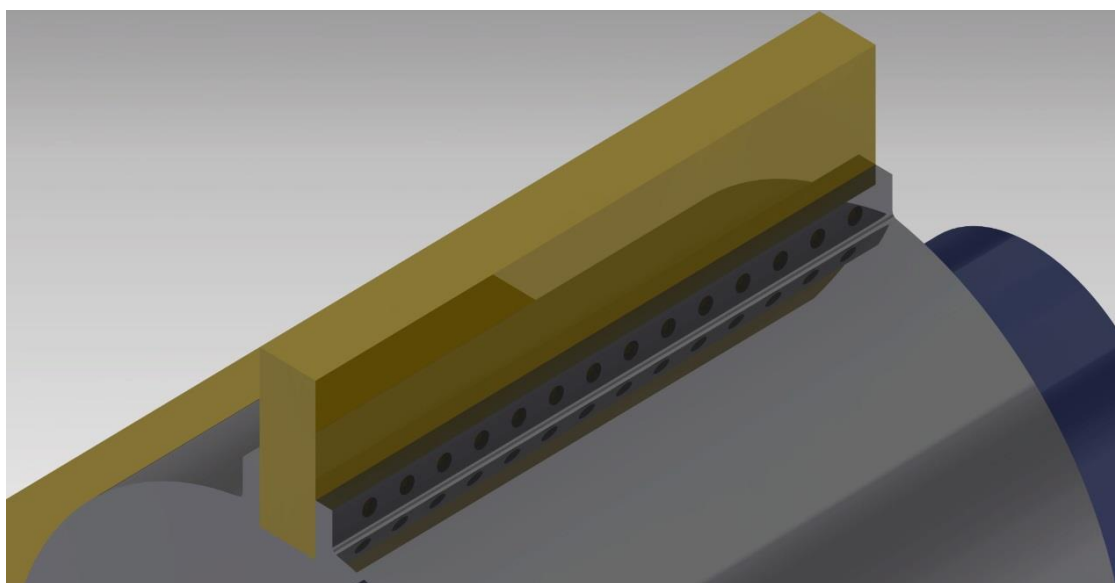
Disposição dos 14 parafusos na montagem do rotor.
